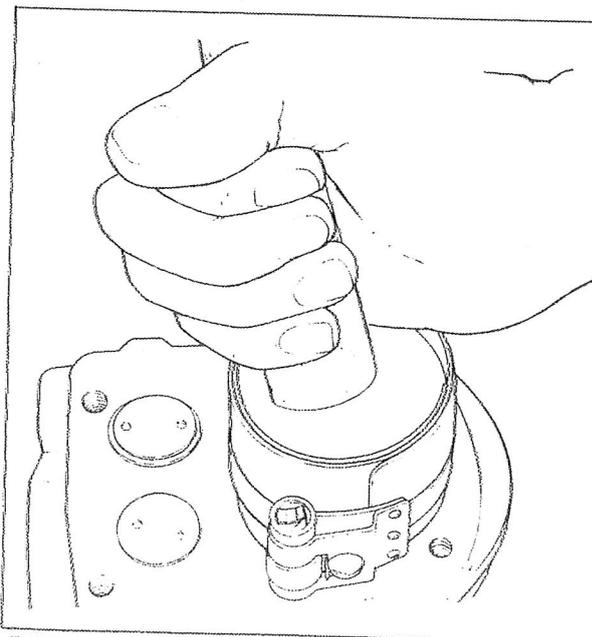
MONTAGE DU PISTON A L'AIDE D'UN
